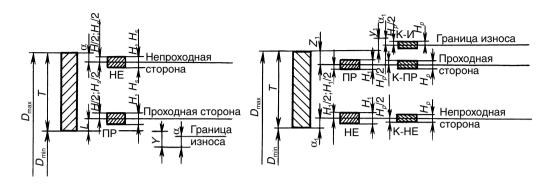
Схемы расположения полей допусков калибров по ГОСТ 24853—81
